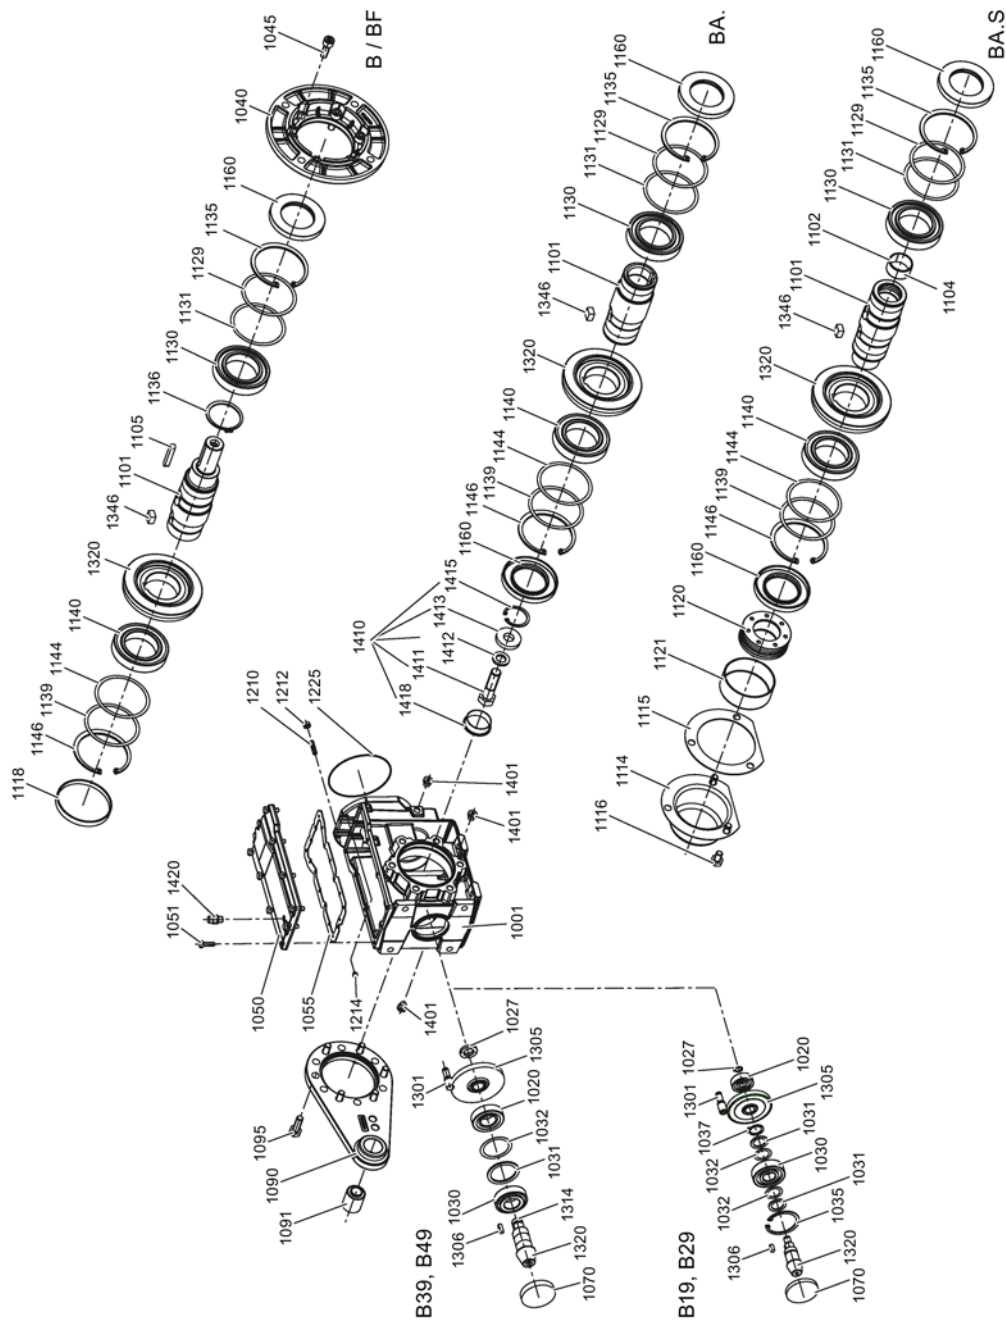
Плоские редукторы F типоразмеров 29-189
